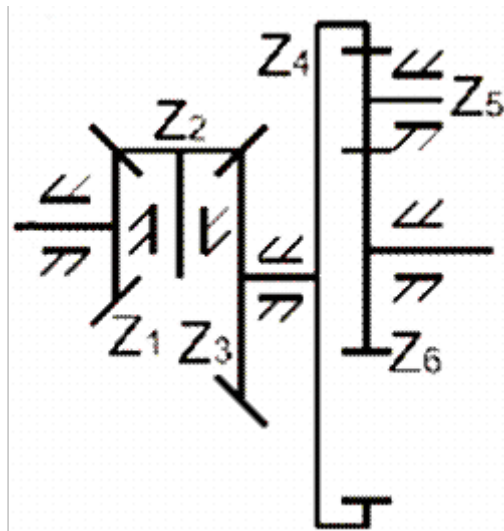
Многоступенчатая зубчатая передача с паразитными колесами
